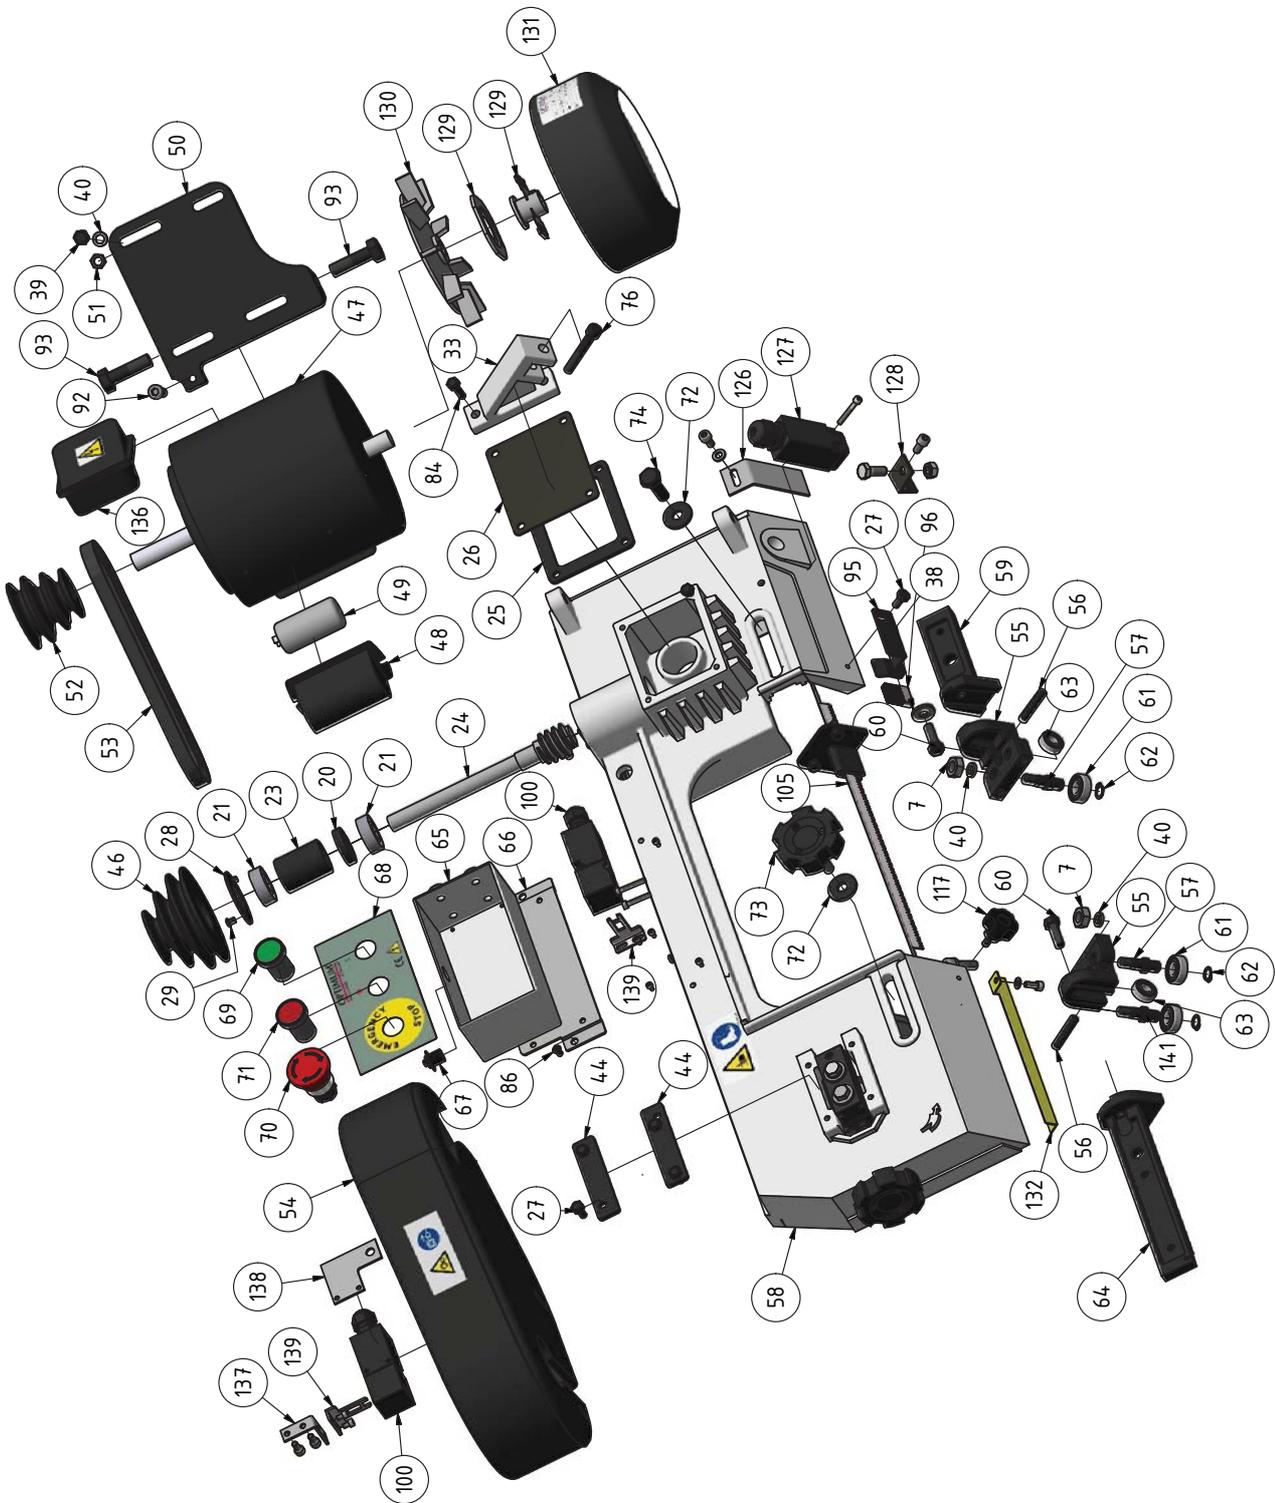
Ersatzteilzeichnung 1 von 4 - Parts drawing 1 of 4
